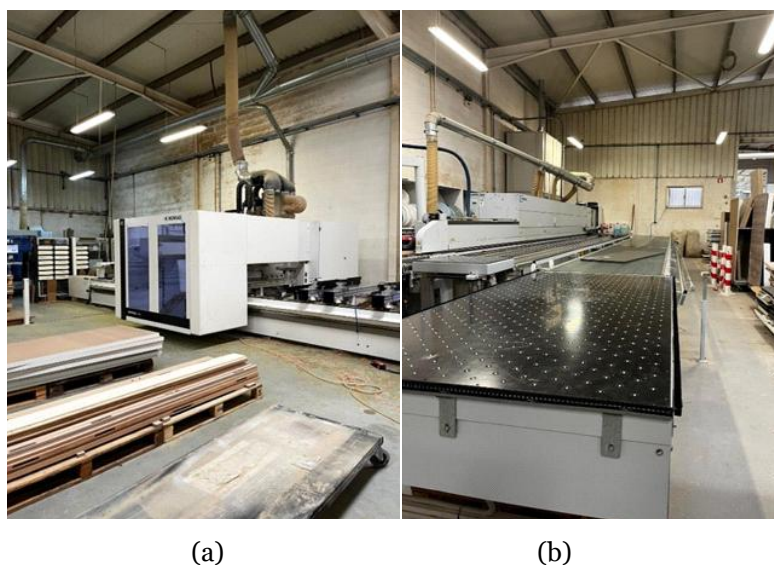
Vista da Máquina CNC (a) e da Máquina Orladora (b).
